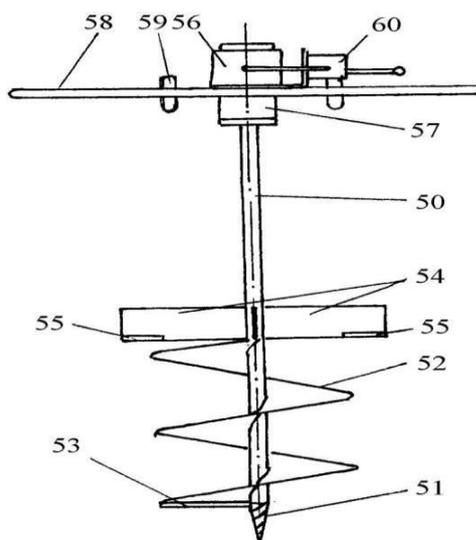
Ямокопатель лесопосадочного агрегата
